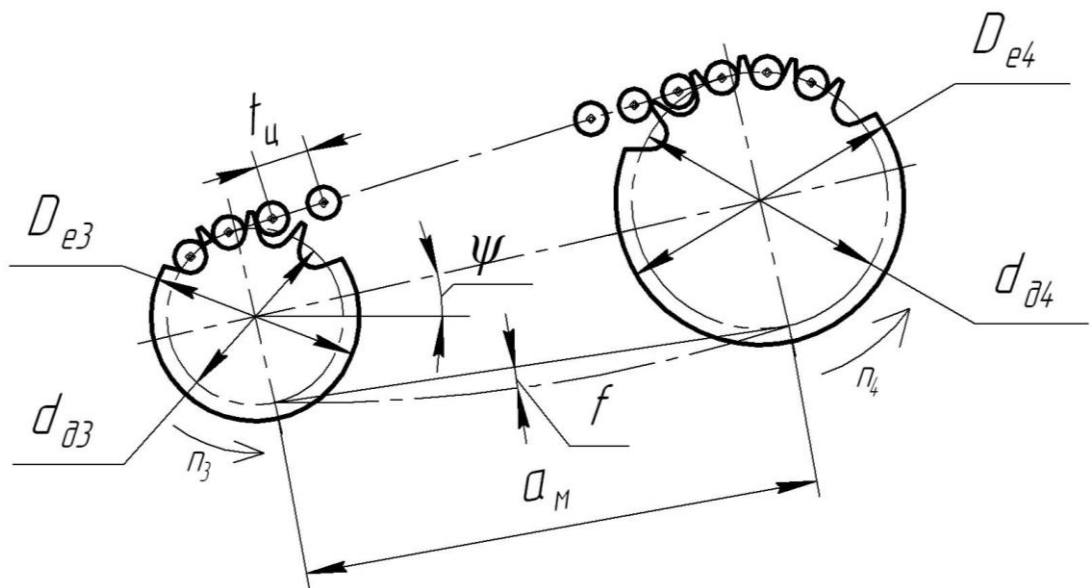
Схема привода ленточного конвейера и цепной передачи
